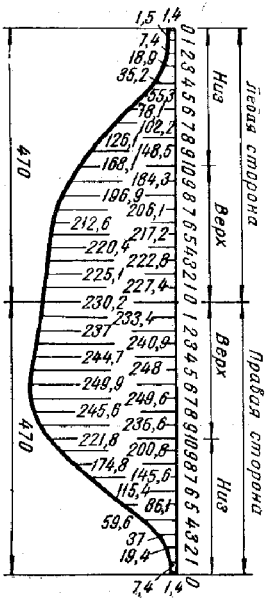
Развертка конца отрезка сварного трюпкина.
